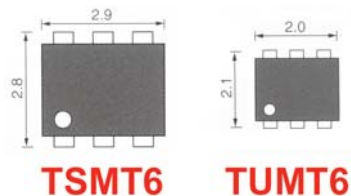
Габаритные размеры корпусов TSMT6 и TUMT6 (в мм)
